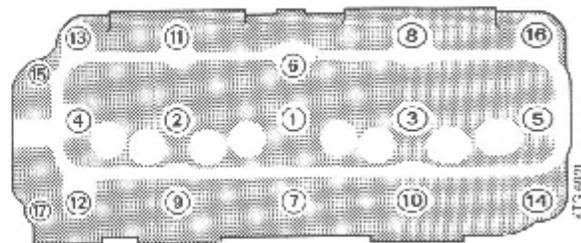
Anzugsschema für Zylinderkopfschrauben
